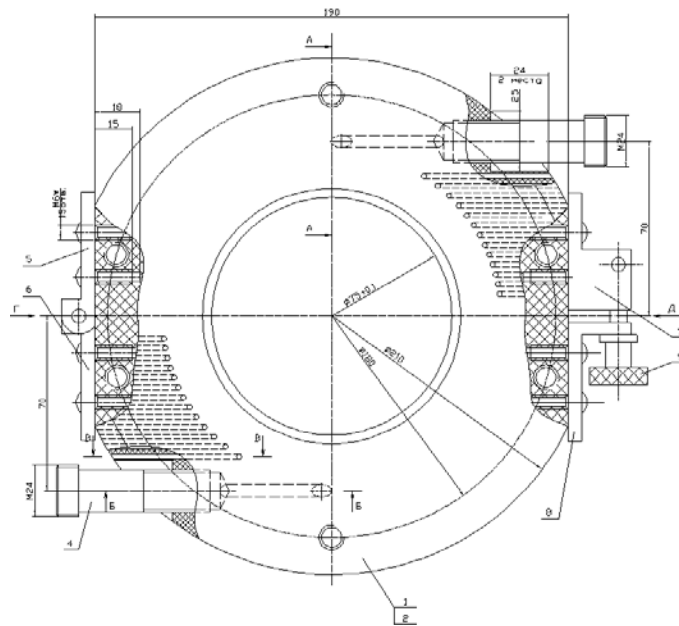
Конструкция специальной пневмодинамической камеры для упрочнения шеек коленчатых валов: 1 – крышка; 2 – крышка; 3 – сегмент; 4 – резьбовой клапан; 5, 6 – элемент петли; 7 – хомут; 8 – упор; 9 – головка резьбовая; 10, 11 – ось
